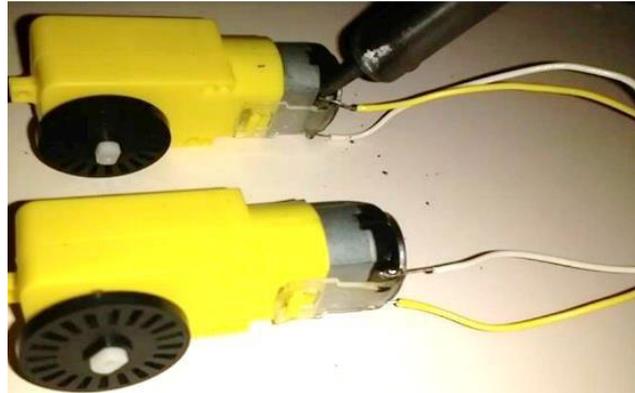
Motorreductores con cables soldados (elaboración propia).
